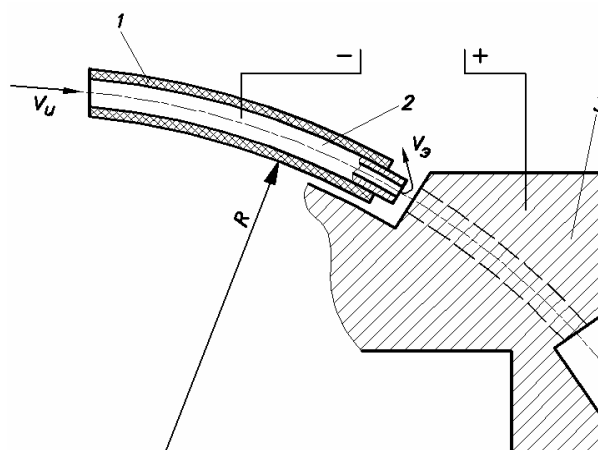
Схема обработки канала с криволинейной осью:
